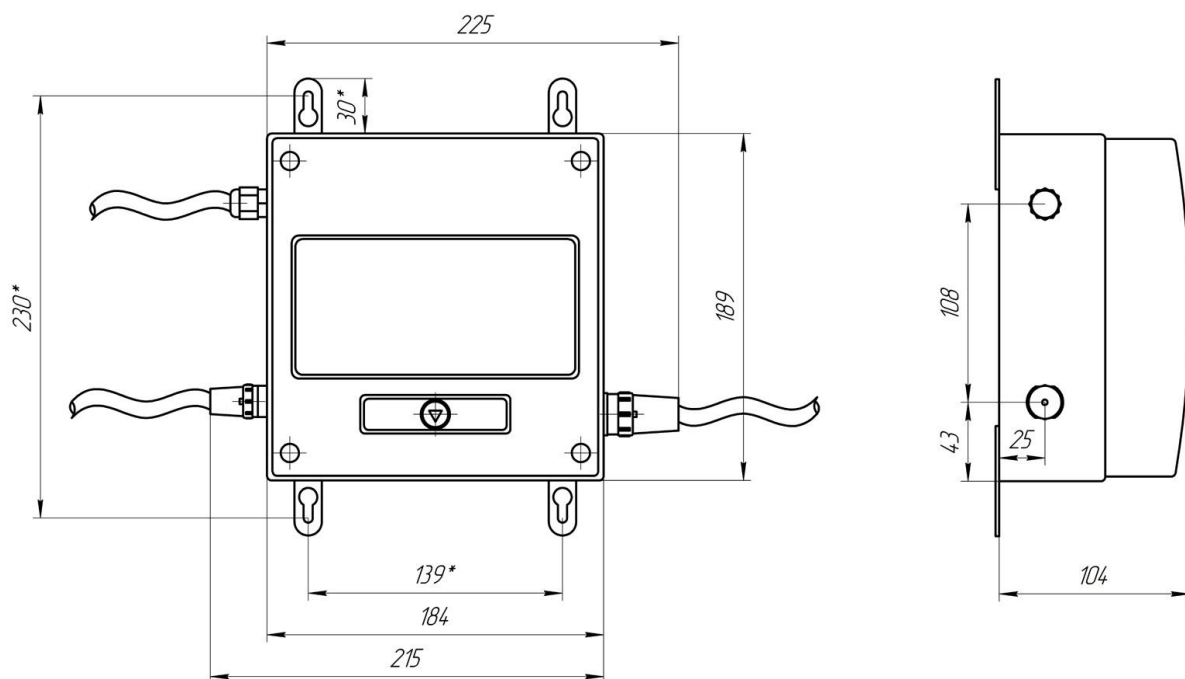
Габаритный чертёж ВЭП СКЭ версии 1
